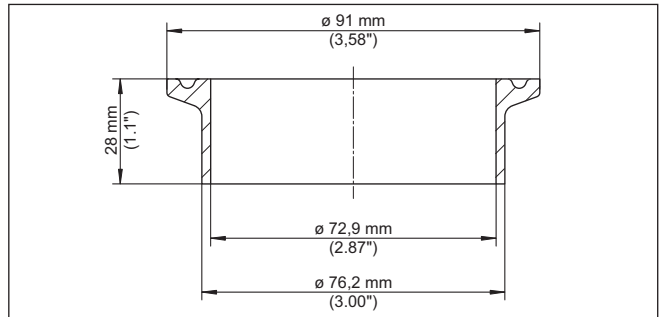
Maße Einschweißstutzen Clamp 3" (DIN 32676, ISO 2852) - VEGABAR 82
